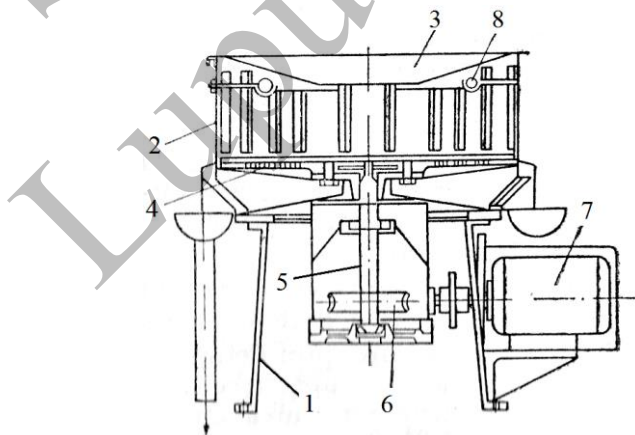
Schema unei centrifuge de opărire și curățire a burților: 1- postament; 2- tobă fixă; 3- gură încărcare; 4- disc rotativ; 5- ax vertical; 6- reductor melc; 7- electromotor; 8- conductă admisie apă fierbinte
